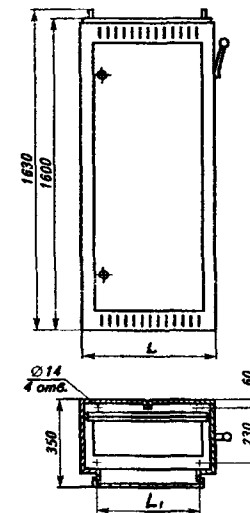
Габаритные, установочные размеры шкафов ШРС.
